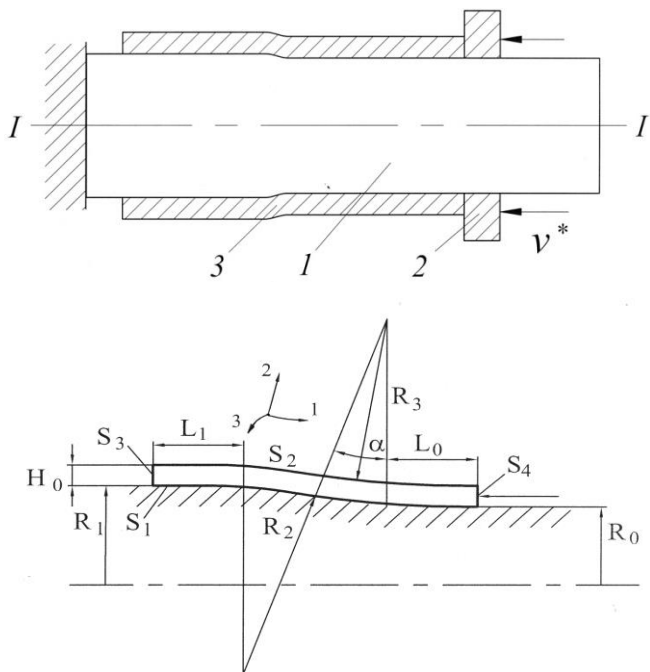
Схема калибровки раздачей трубной заготовки по жесткому
